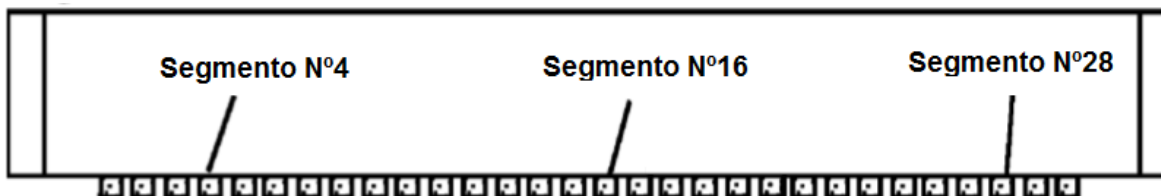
Detalhe da lâmina utilizada nos ensaios (adaptado de Wang, C. Y. e Clausen, R., 2003).
